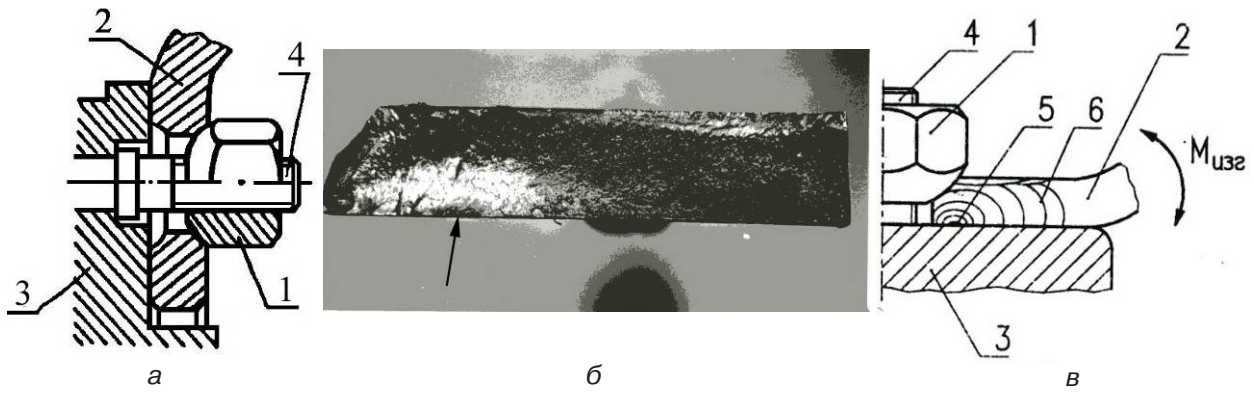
Крепления дискового колеса по ГОСТу 10409-74 (а), фрактография разрушения диска (б) и схема роста трещины фреттинг-усталости (в): 1 – гайка; 2 – диск; 3 – ступица; 5 – шпилька; 5 – очаг зарождения трещины; 6 – фронт роста трещины; стрелкой показан очаг зарождения трещины на фотографии излома
